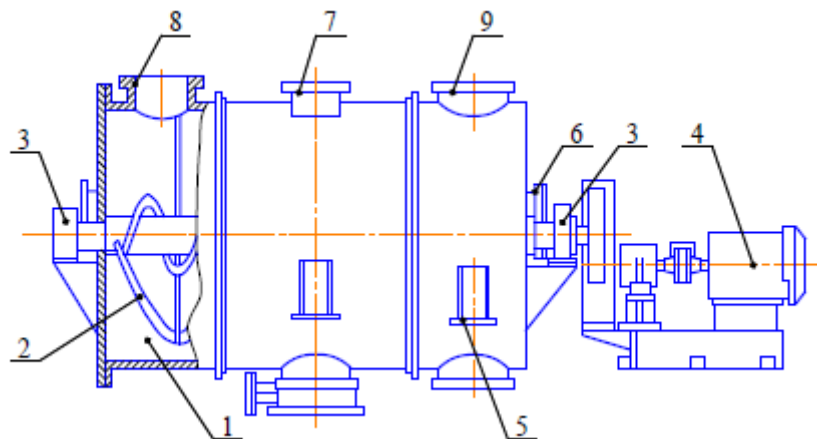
Змішувач стрічковий горизонтальний типу СЛН-10: 1 – корпус змішувача; 2 – стрічкова мішалка; 3 – опорні підшипники; 4 – привід змішувача; 5 – опорні лапи; 6 – люк для огляду; 7 – штуцер для вентиляції; 8, 9 – штуцери для завантаження матеріалу; 10 – штуцер для вивантаження матеріалу
